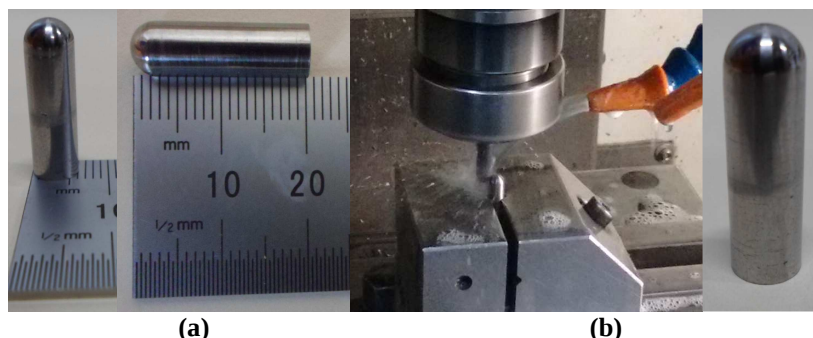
Pino de Ferro Fundido Nodular (a) – dimensões em mm (b) – usinagem da ponta esférica (O Autor, 2016)
